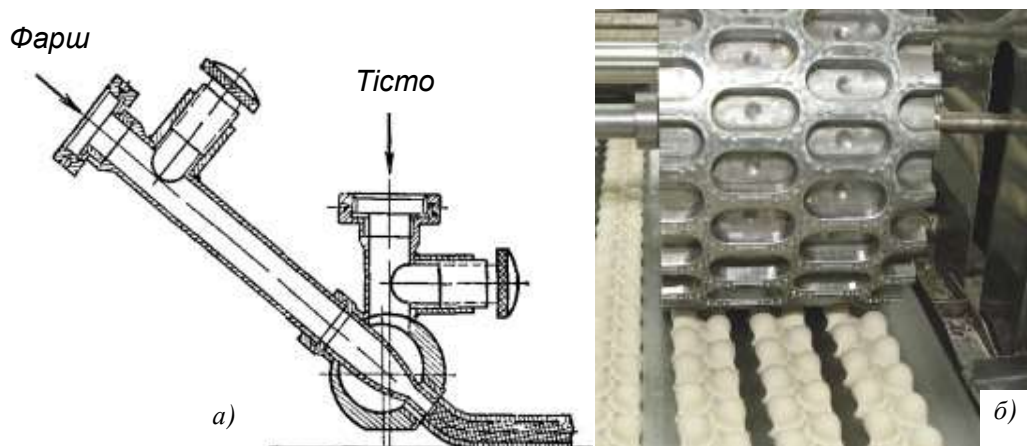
Формувальний пристрій а) і штампувальний барабан б).
